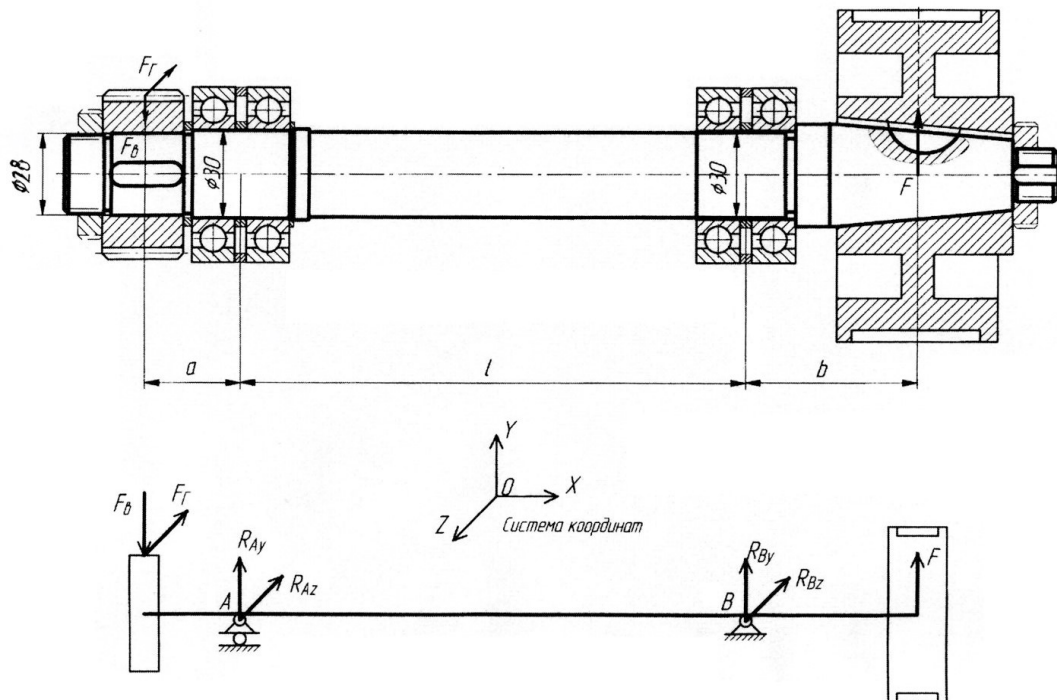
Ескіз і розрахункова схема «Вал»
